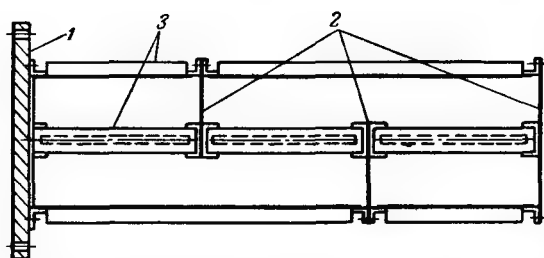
Каркас с трубной доской и перегородками для водоподогревателя с U-образными трубками.
